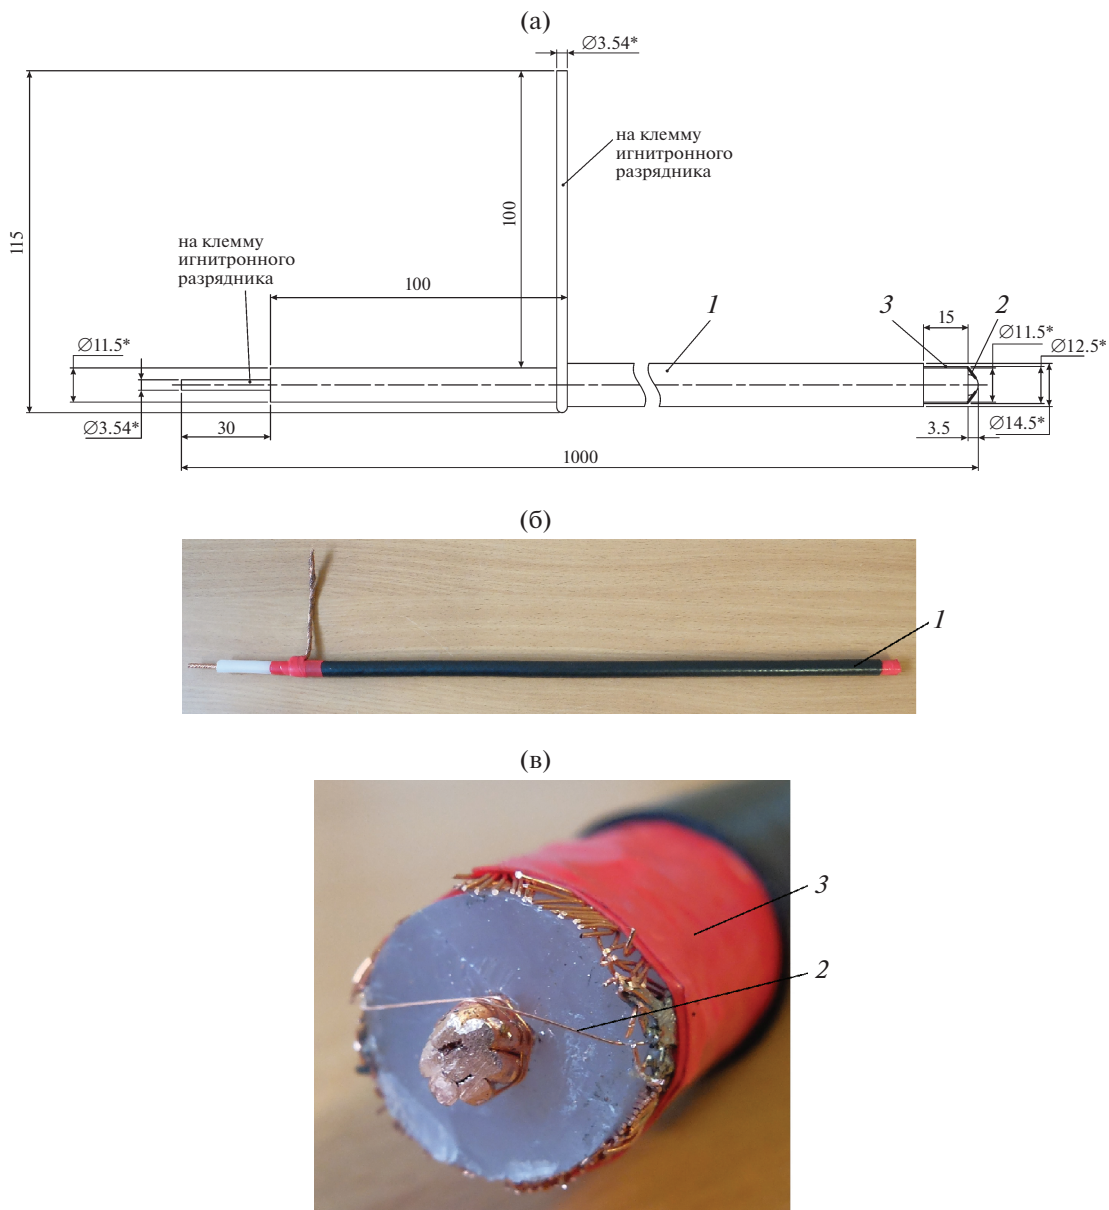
Конструкция инициатора (а) и его внешний вид (б, в). 1 – отрезок коаксиального кабеля; 2 – иницирующая проволочка; 3 – изоленга.
